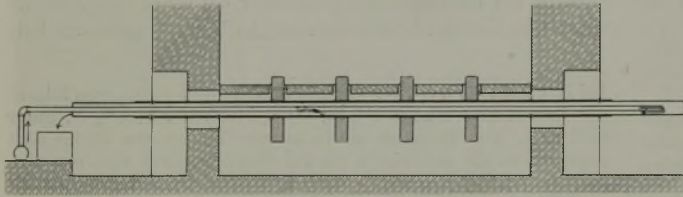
Tragscheiben auf wassergekühlter Hohlwelle mit Innenkühlrohr.
